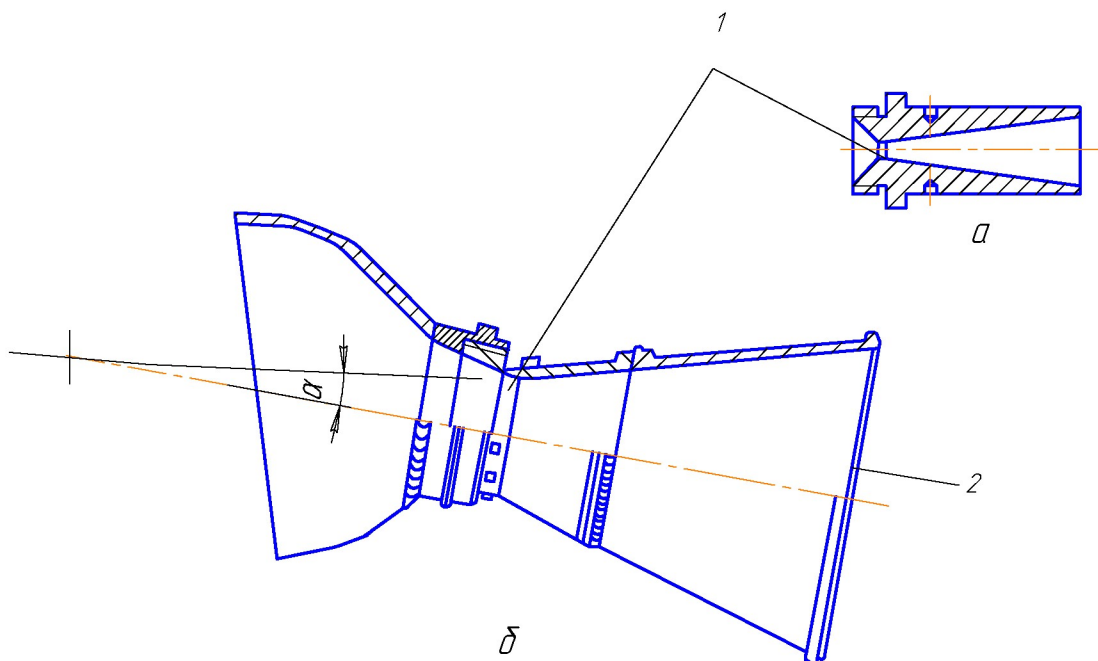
Простые сопла РДТТ: а – точеное, б – сварное, установленное под углом к оси двигателя: 1 – цилиндрическая проточка; 2 – заглушка
